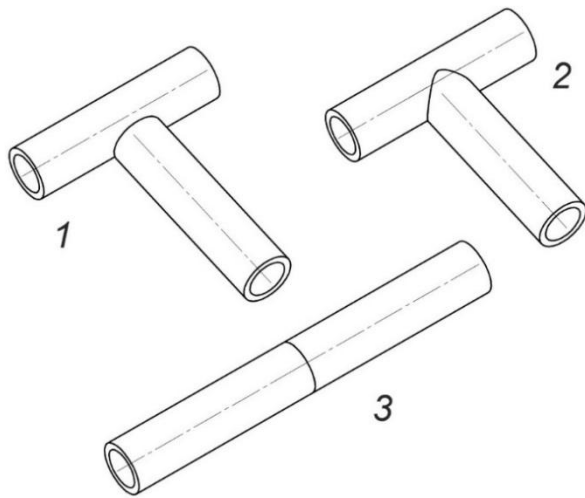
Виды сварных стыковок труб в раме квадроцикла
